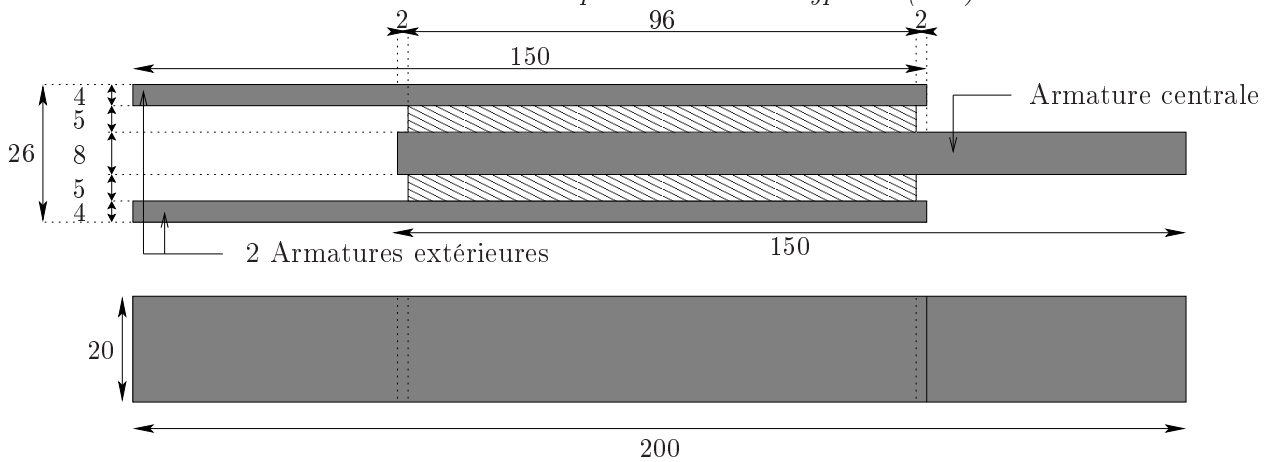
Dimensions éprouvette de double cisaillement (mm).
